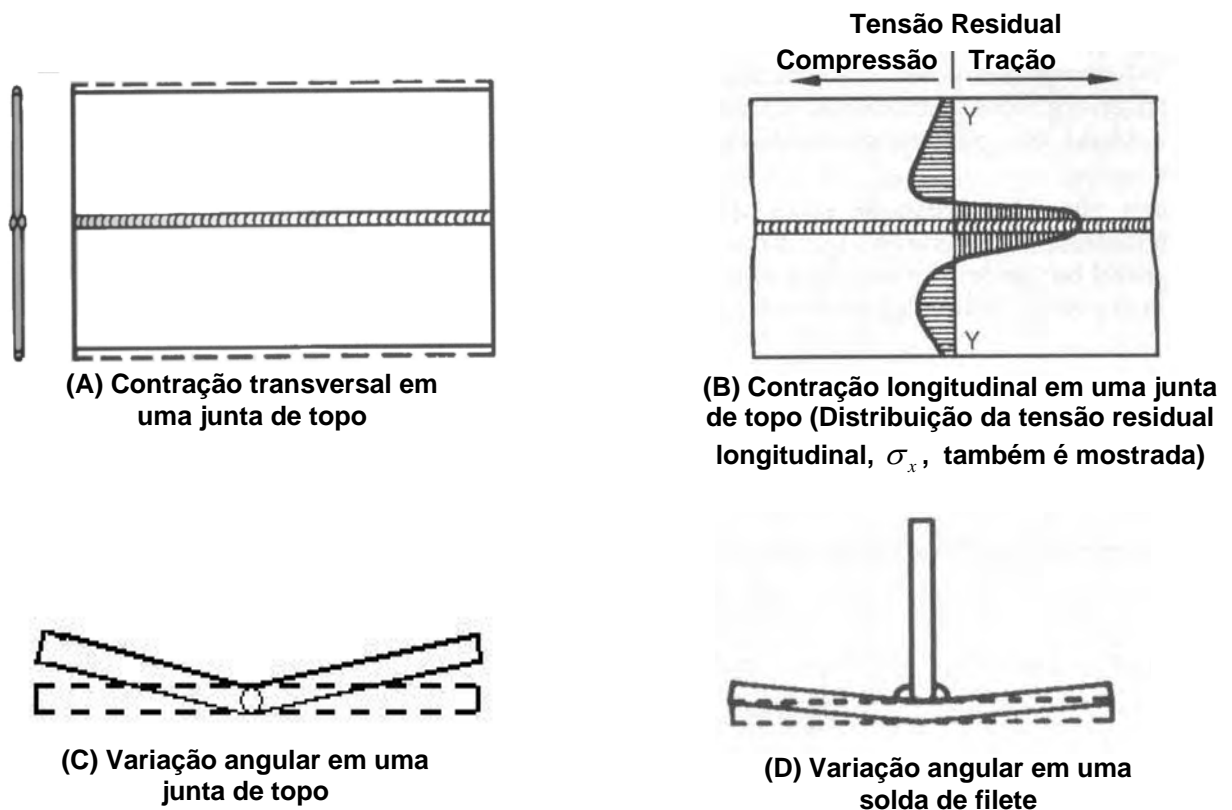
Variações dimensionais fundamentais que ocorrem em soldagem (AWS, 2001)
